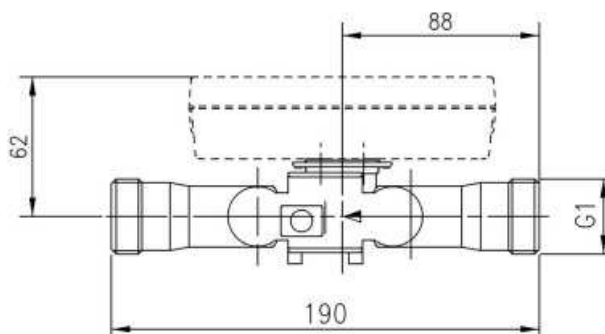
Översikt dimensioner total längd 190 mm (gängad)
